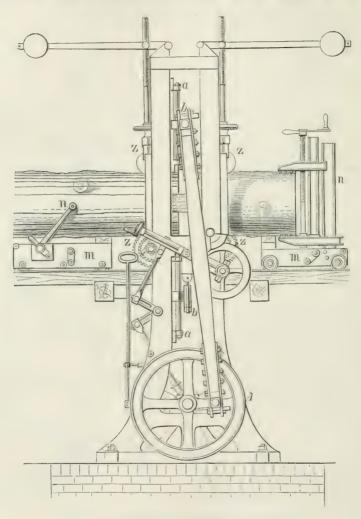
Konftruttion einer Dampffage mit Bollgatter.
